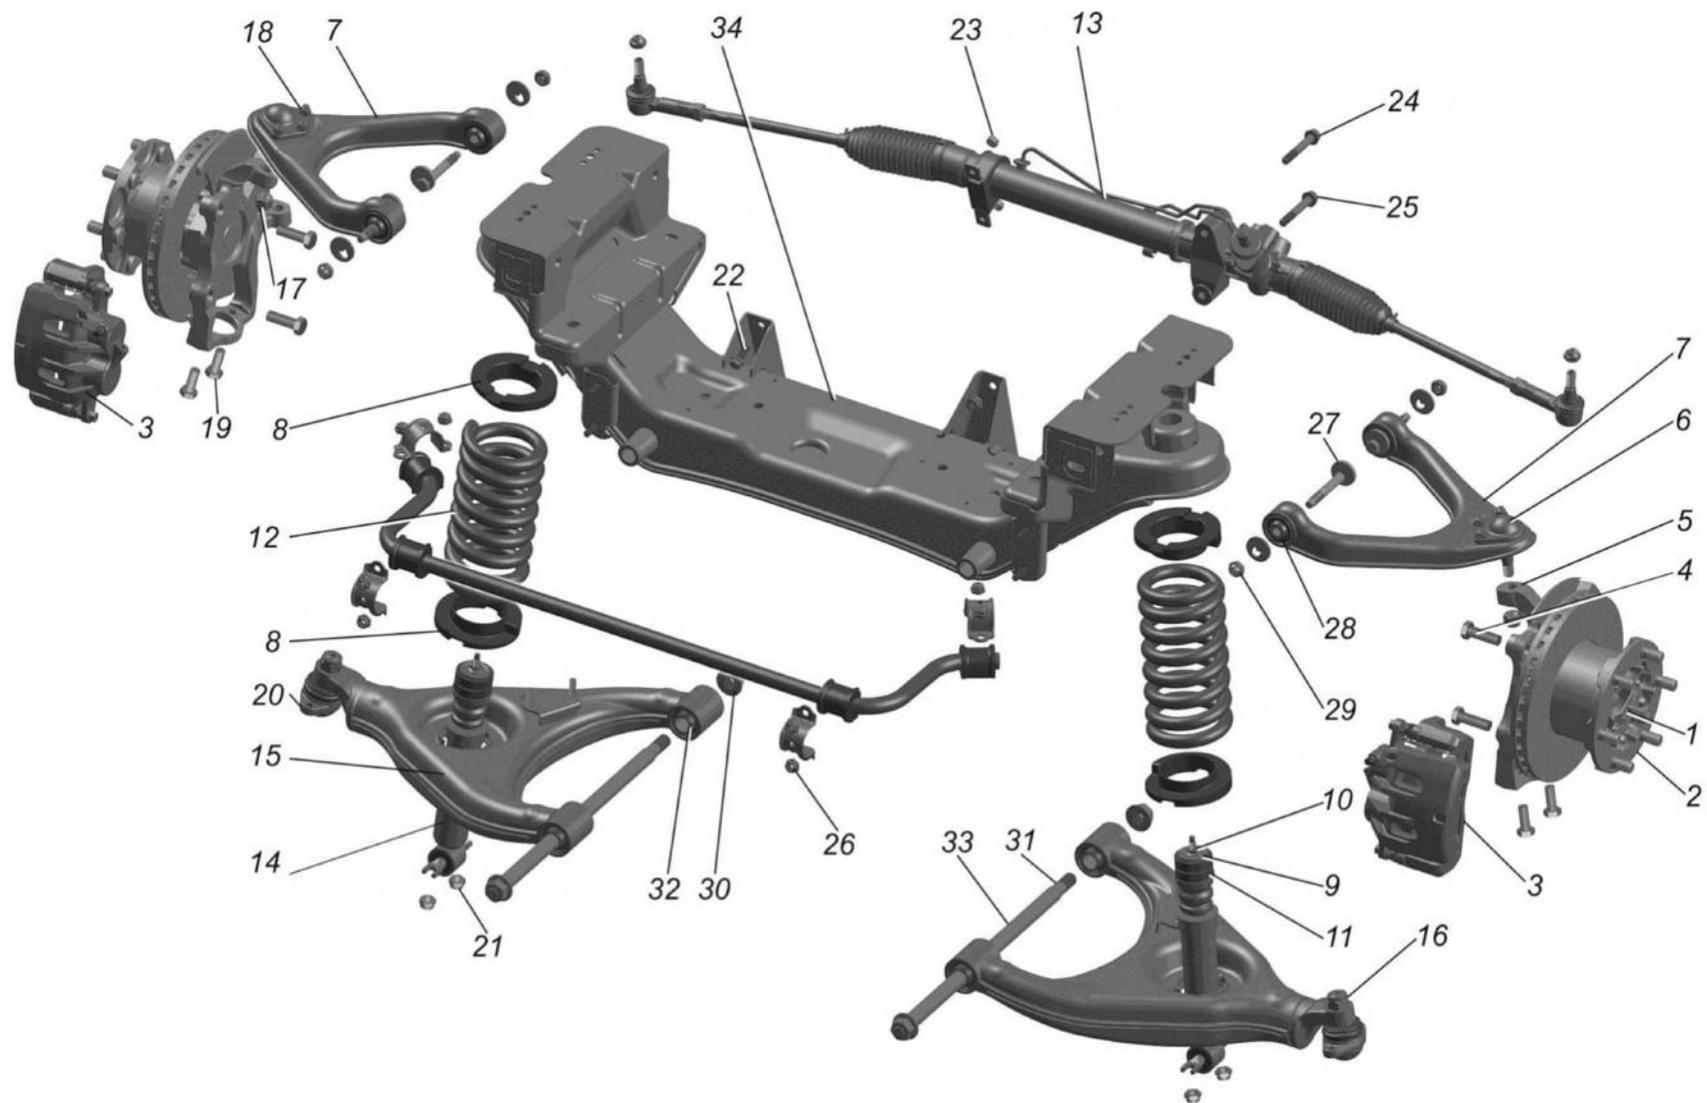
Детали передней подвески: 1 – кронштейн крепления колпака колеса; 2 – стойка со ступицей и тормозным диском; 3 – тормозная скоба; 4 – болт крепления тормозной скобы к стойке; 5 – стойка; 6 – шарнир шаровой верхней; 7 – рычаг верхний; 8 – прокладка пружины; 9 – шайба; 10,16,17,18,21,23,26,29,30 – гайки; 11 – подушка; 12 – пружина; 13 – механизм рулевой; 14 – амортизатор; 15 – рычаг нижний; 19,22,24,25 – болты; 20 – шарнир шаровой нижней; 27 – регулировочный болт в сборе с эксцентриковой шайбой; 28 – сайлентблок верхних рычагов; 31 – втулка; 32 – сайлентблок нижних рычагов; 33 – ось нижних рычагов, 34 – подрамник
